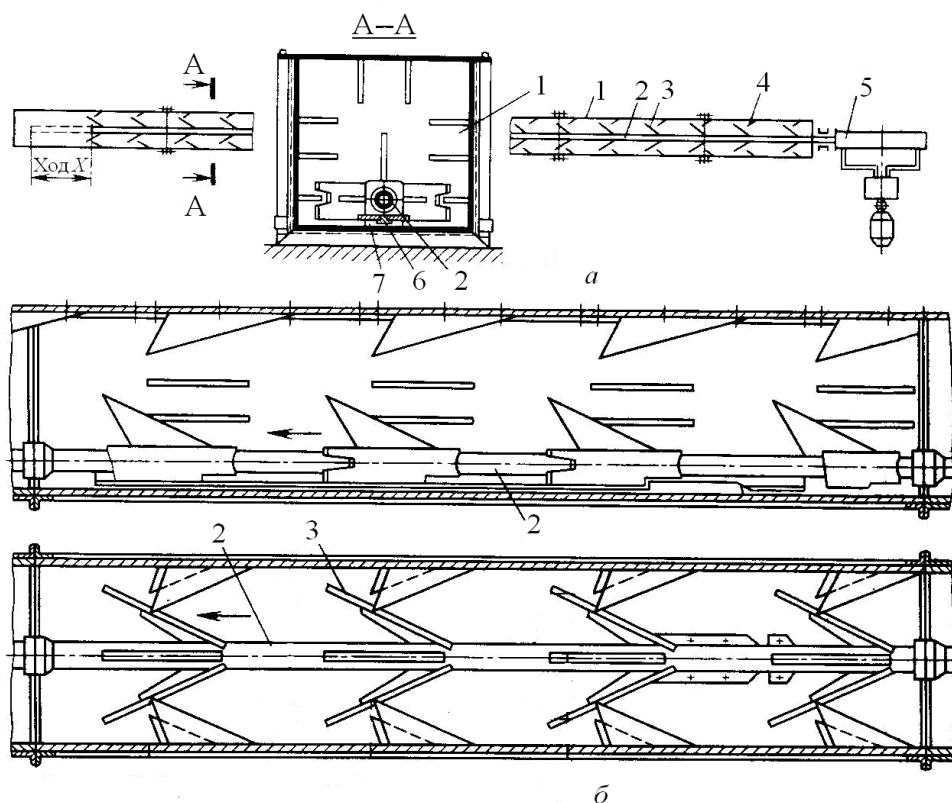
Штанговый скребковый конвейер для перемещения витой стружки:
